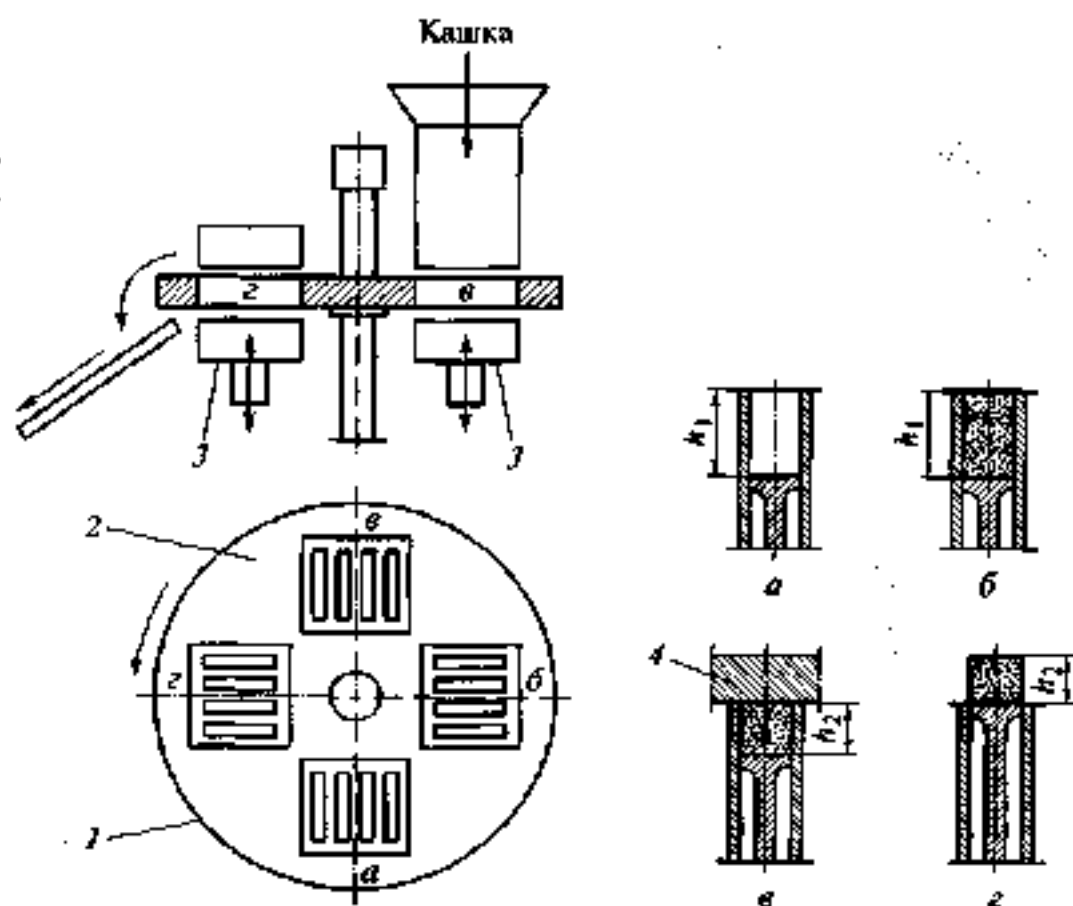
Карусельный пресс с возвратно-поступательным движением пуансона:
